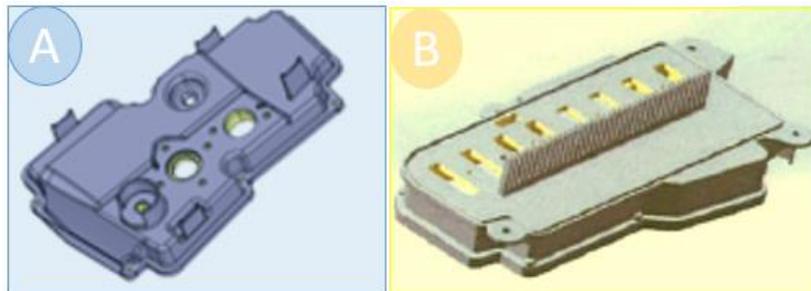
E1XXXX55630C0 (A) e E1XXXX55630C0 (B)
